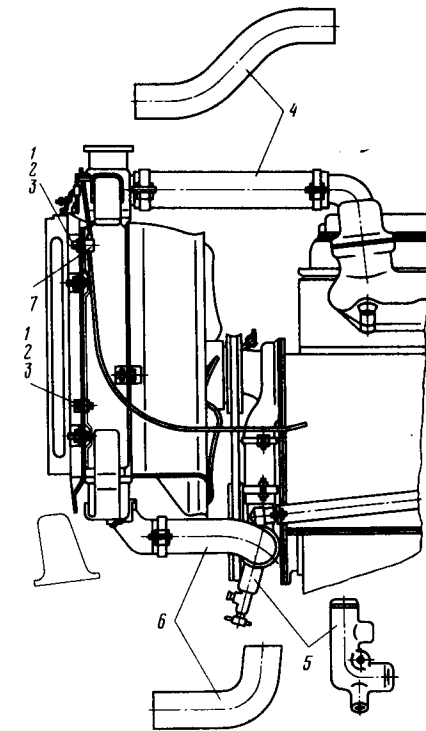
Установка подводящего патрубка водяного насоса (вид сбоку):
